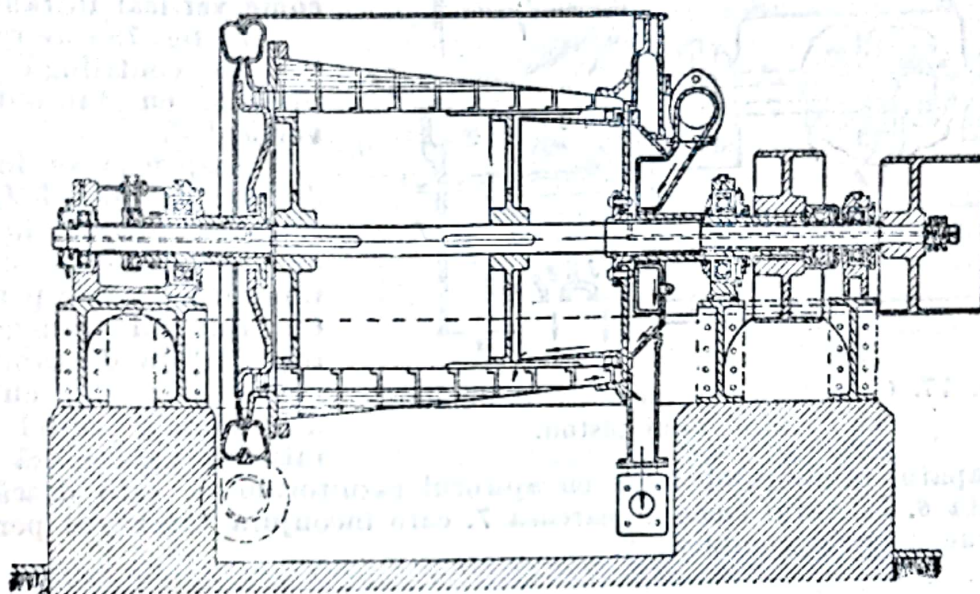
Centrifugă cu tambur conic și cu arbore orizontal.
